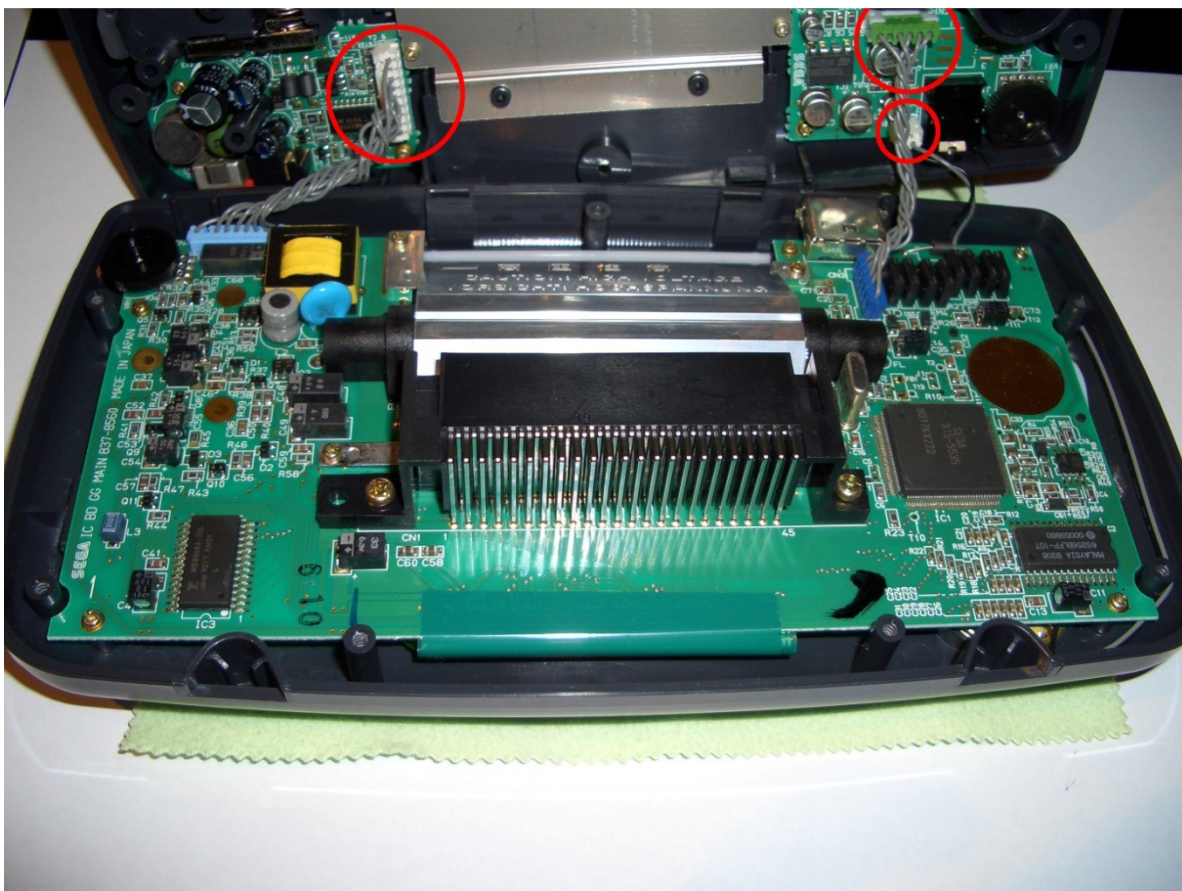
Game Gear geöffnet, Kabel an Markierung abziehen
